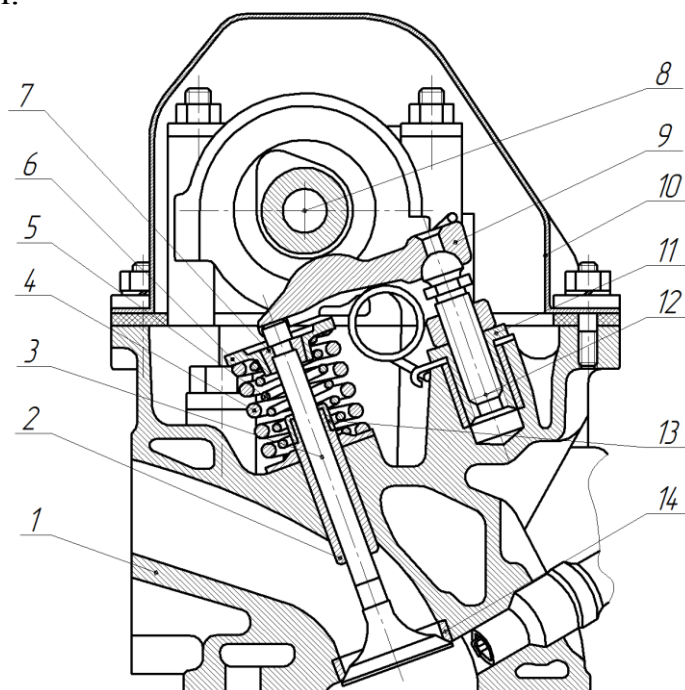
Газораспределительный механизм типа ОНС:
